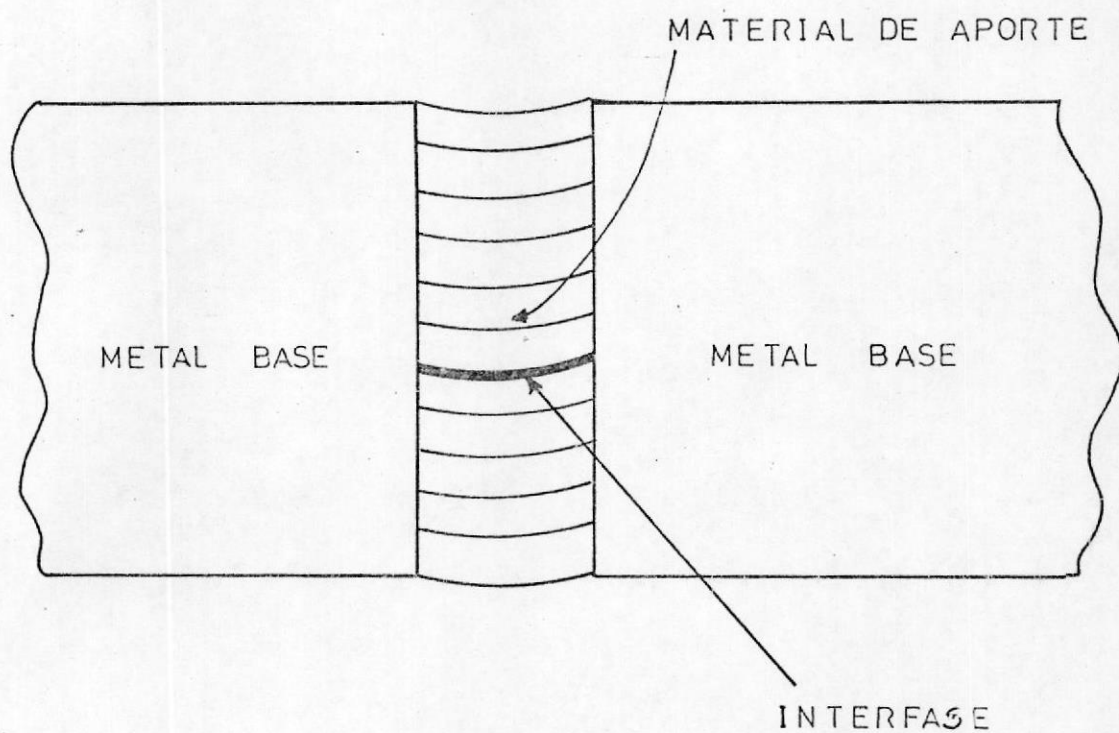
FISURA TRANSVERSAL EN UN CORDON DE SOLDADURA (10)
